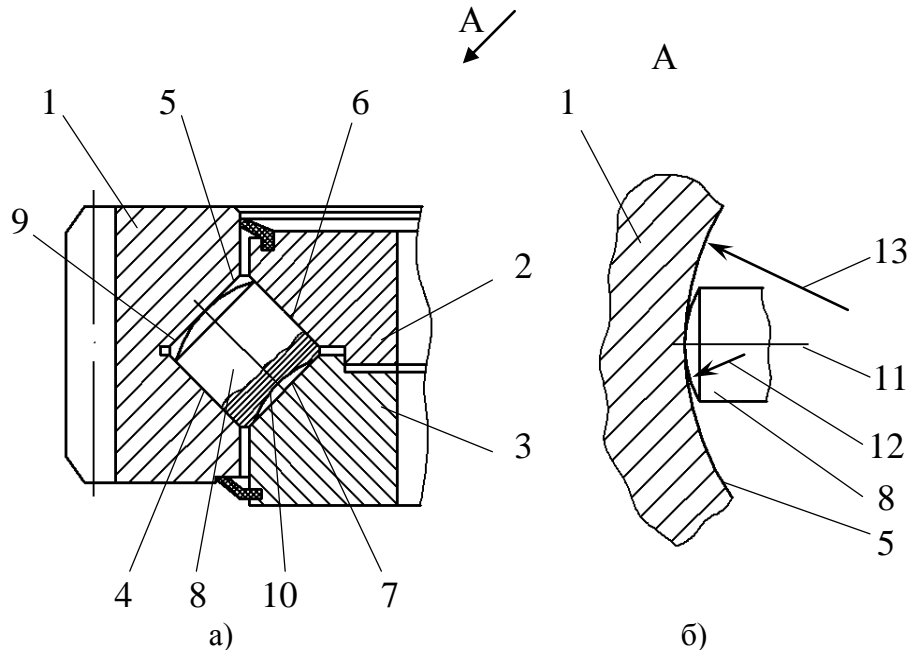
Принципова конструкція опорно-поворотного пристрою з модифікованими роликами: а – загальний вигляд лівої частини в перерізі; б – вид у напрямі А (стрілка А) на внутрішню поверхню бігової доріжки у місці дотику ролика
